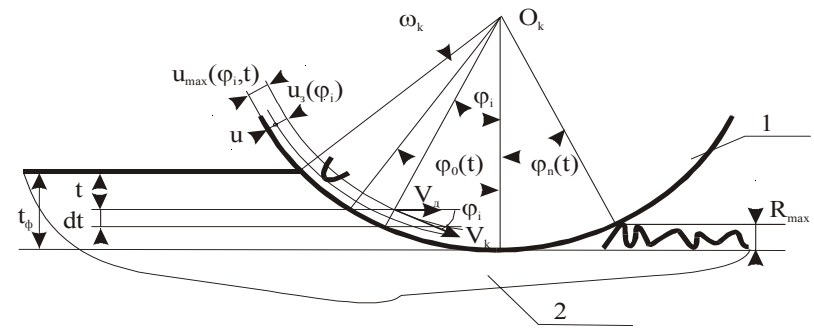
Схема плоского шлифования периферией круга 1- шлифовальный круг, 2 -заготовка.
